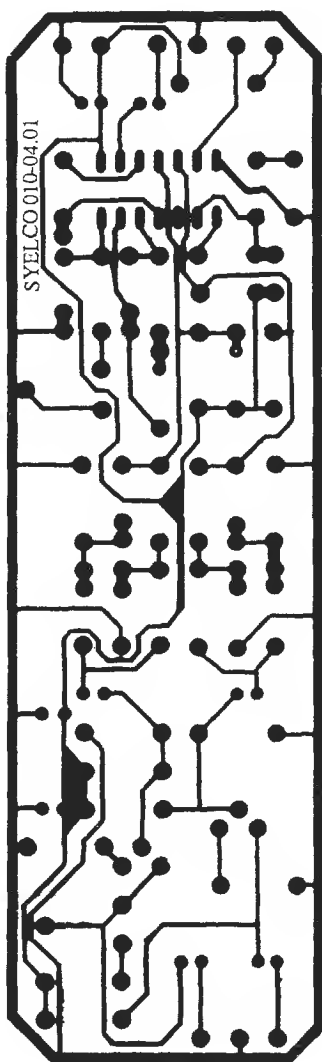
Circuito stampato del decodificatore stereofonico.
